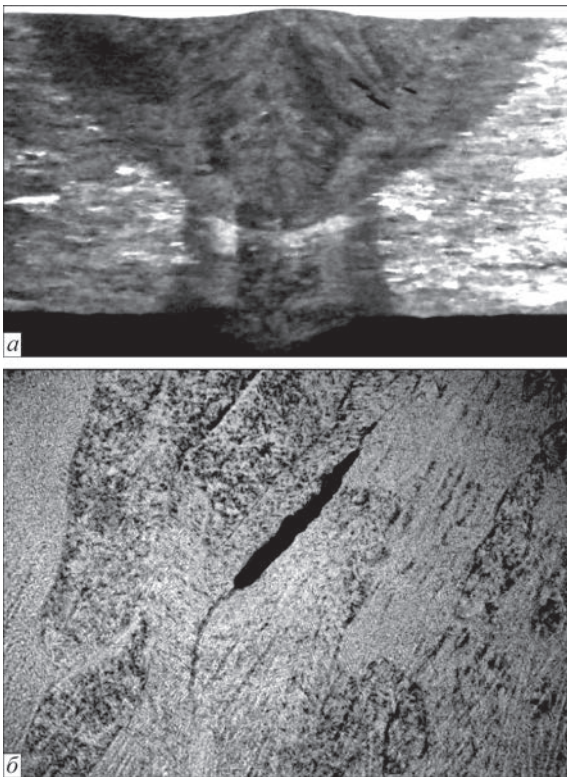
Структура образца № 3: *a* — поперечный макрошлиф сварного соединения; *б* — участок шва с трещиной ( $\times 500$ )
